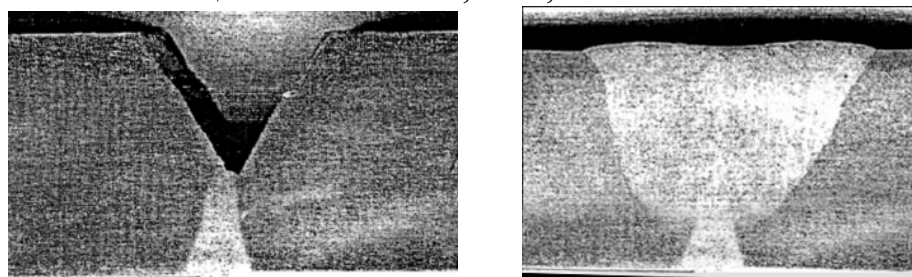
Макрошлиф сварного соединения пластины с толщиной стенки 16,8 мм, выполненного: а) двухлучевой лазерной сваркой; б) дуговой сваркой под флюсом с другой стороны пластины.
